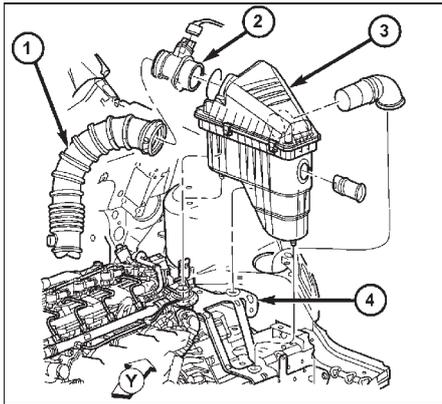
Корпус воздушного фильтра - типичный пример. 1 - воздуховод, 2 - датчик расхода воздуха, 3 - корпус воздушного фильтра, 4 - кронштейн.
